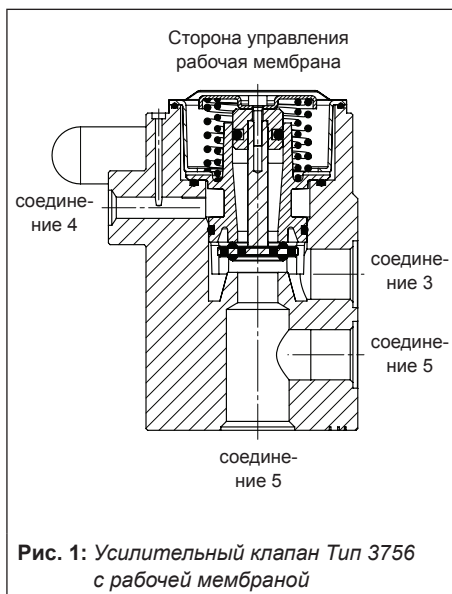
Усилительный клапан Тип 3756 с рабочей мембраной
